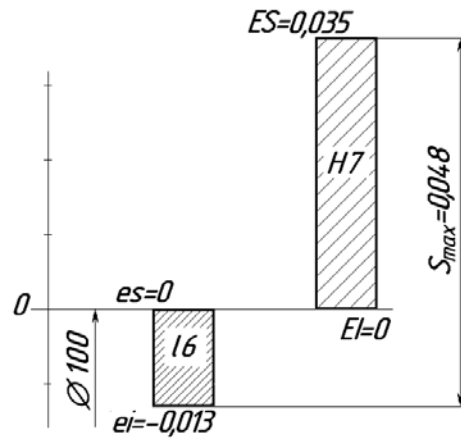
Схема расположения полей допусков соединения наружного кольца подшипника 6—309 с корпусом редуктора
